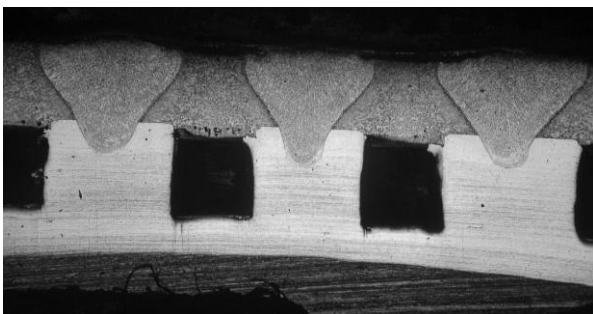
Поперечное сечение образца с зазором между ребрами и рубашкой до сварки
